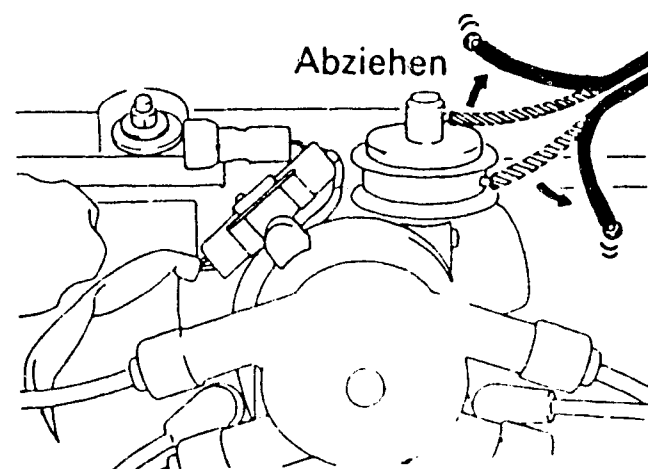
Zur Einstellung des Zündzeitpunktes sind die Unterdruckschläuche abzuziehen und zu verschliessen (oben). Die Markierungen sind an der Kurbelwellen-Riemenscheibe und am Zahnriemenschutz angebracht.
